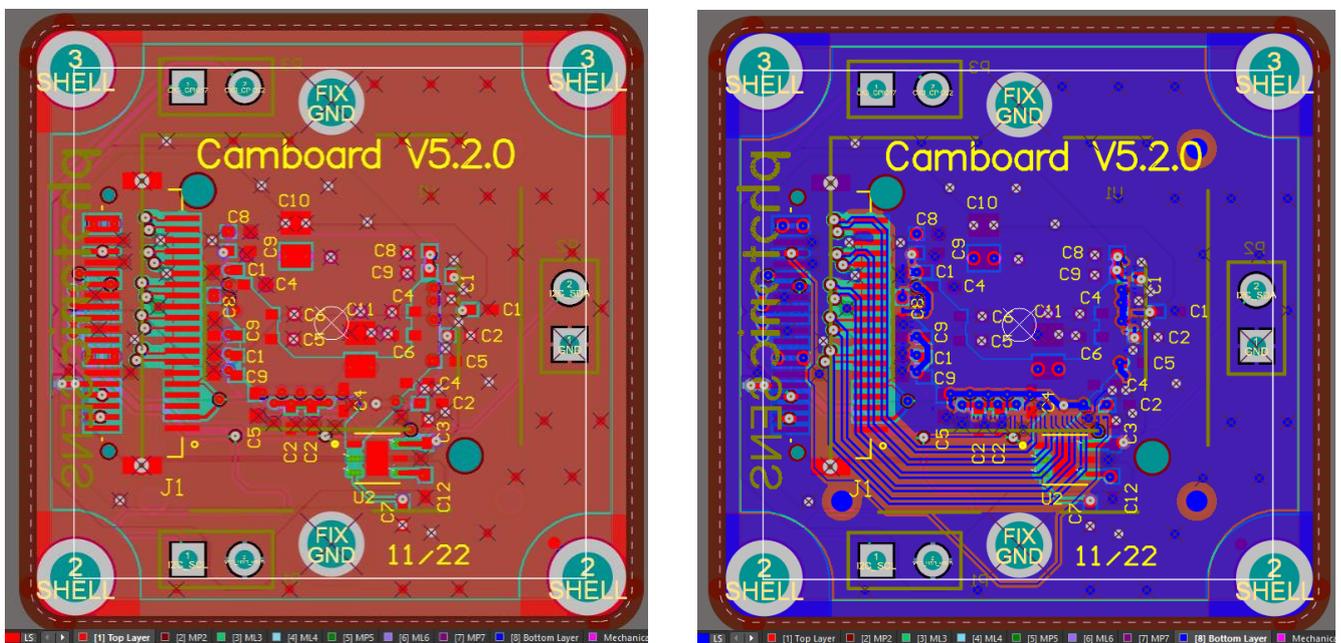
Captura del diseño del PCB Camboard V5.2.0.
